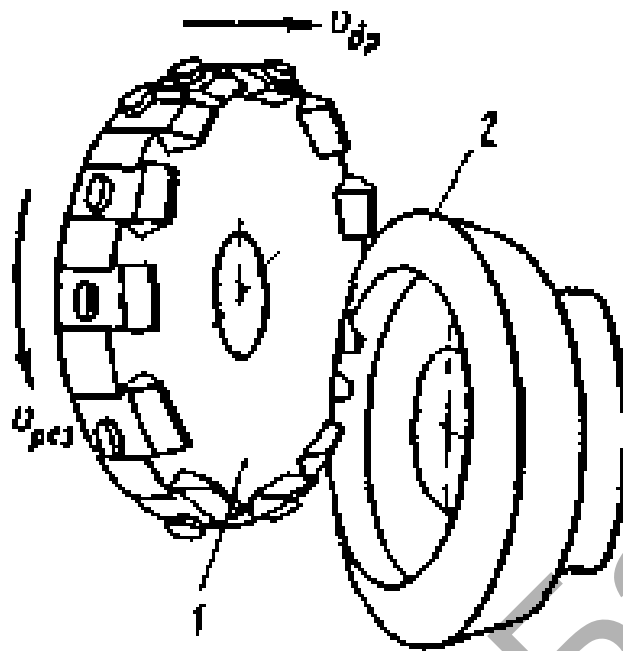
Схема работы зуборезных станков по методу врезания инструмента в заготовку (без обката)
